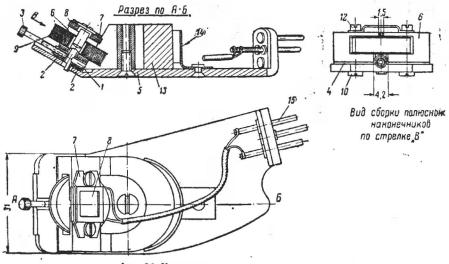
а. Внешний вид звукоснимателя 3-94.
